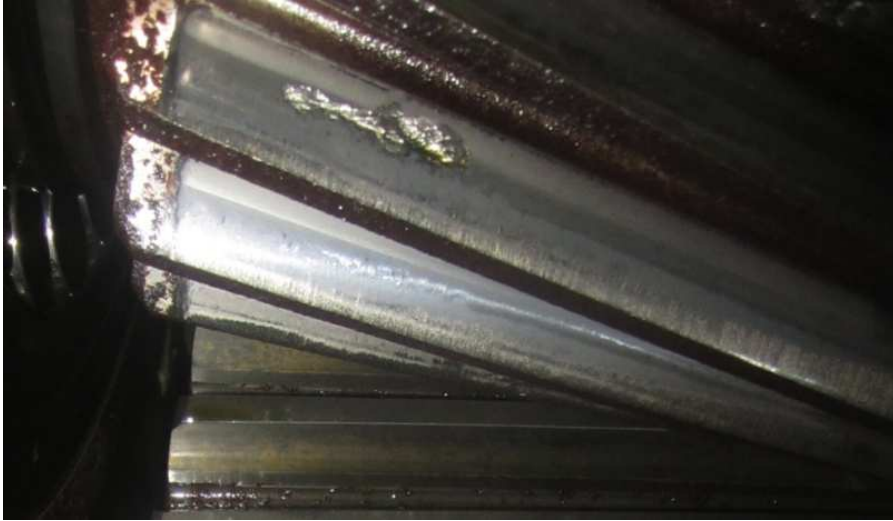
Pitting diente engranaje eje entrada. Fuente [2]
